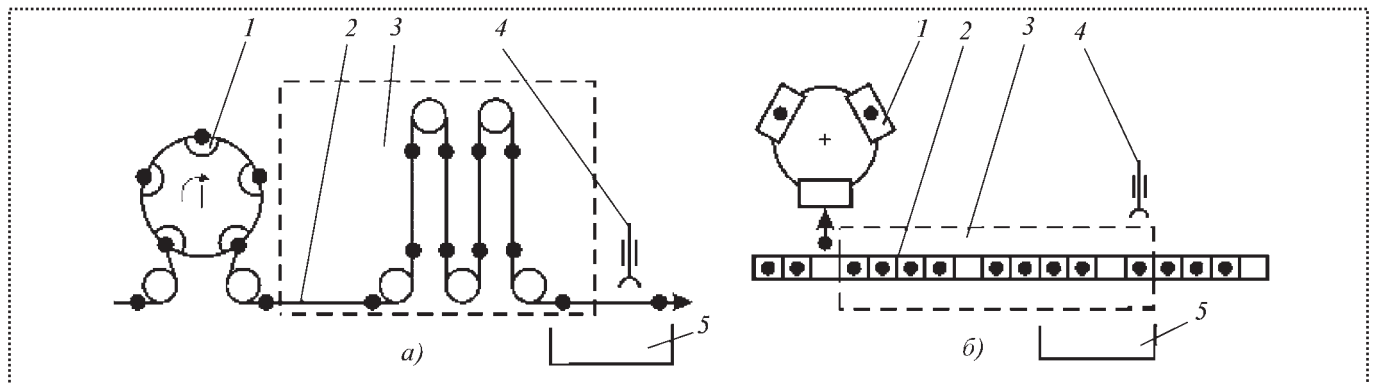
Схемы реализации метода непрерывного выборочного контроля в поточной сборочной линии (а) и в автоматической роторной линии (б)
